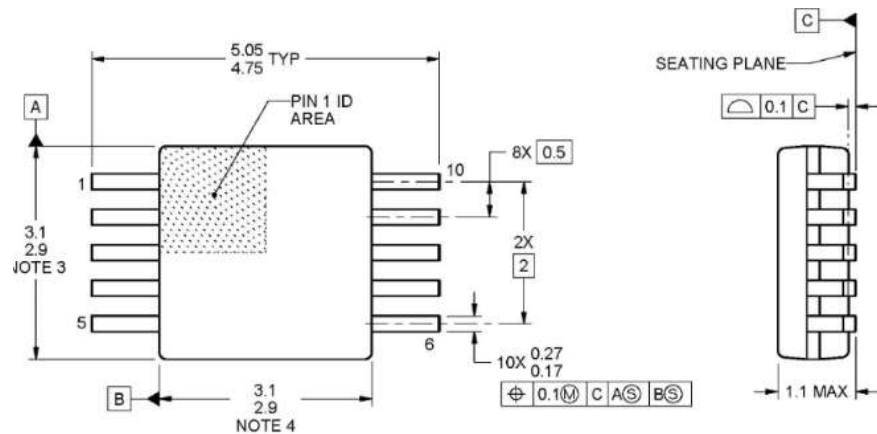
Габаритні розміри мікросхеми INA226
